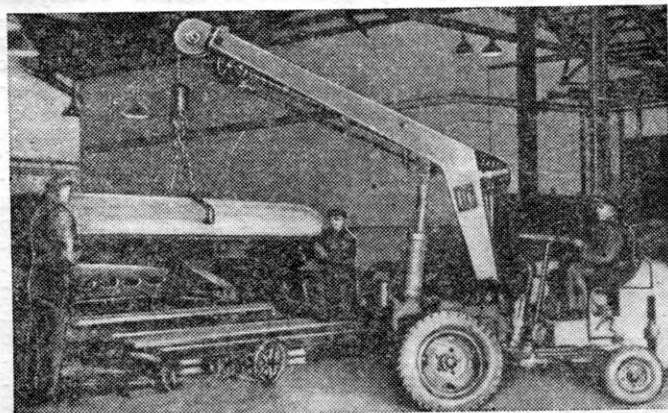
Маневренный малогабаритный автокран (подача к станку крупномерной заготовки)
